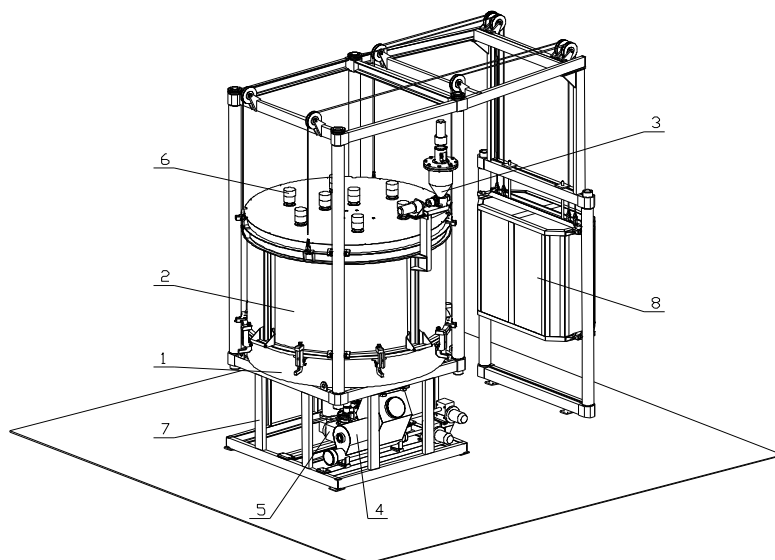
Реактор синтеза УНТ: 1 – корпус верхний; 2 – корпус нижний; 3 – питатель катализатора; 4 – бункер шнековый готового продукта; 5 – привод рабочего стола; 6 – нагревательные элементы; 7 – рама; 8 – противовес
